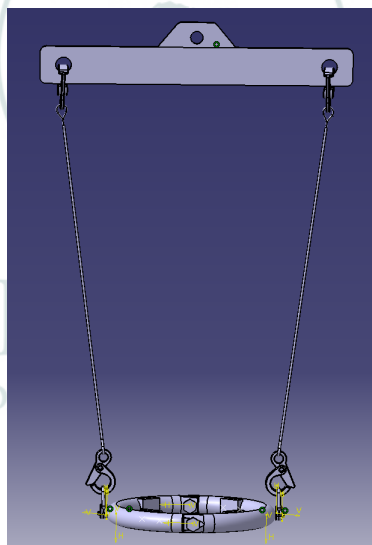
Projeção de suporte do motor do turboshaft - vista frontal
